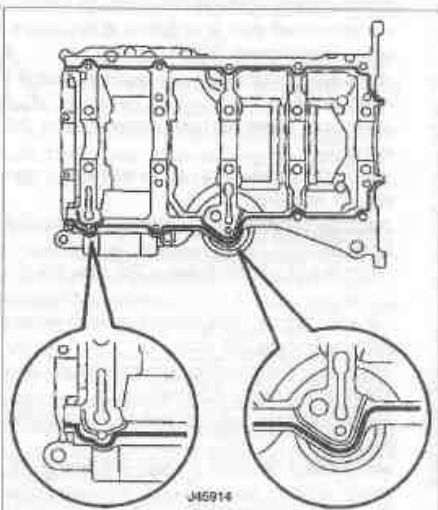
Нанесите герметик в виде валика шириной 2 мм на корпус коренных подшипников (показан бензиновый двигатель)
